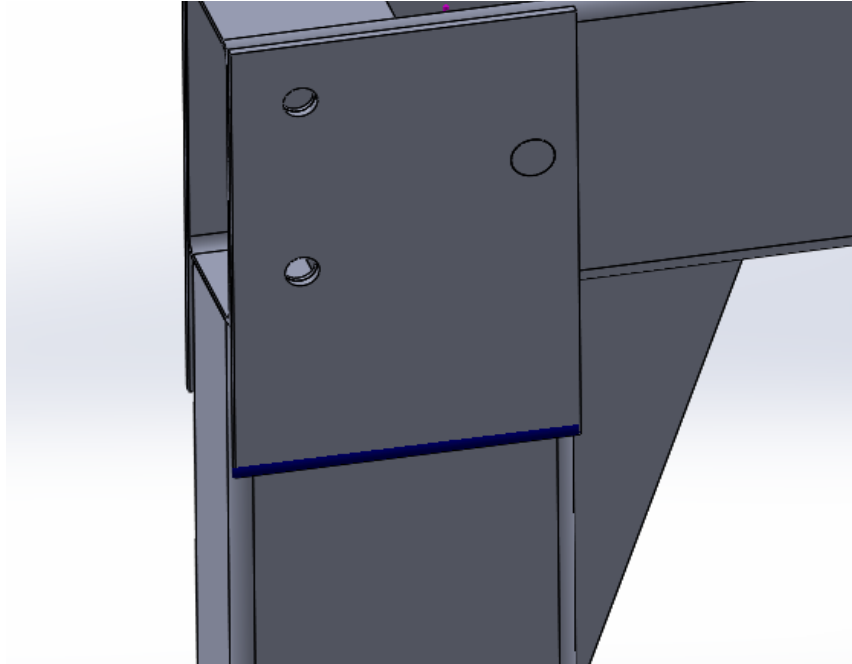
Esquema de soldadura entre la placa superior y la columna.
